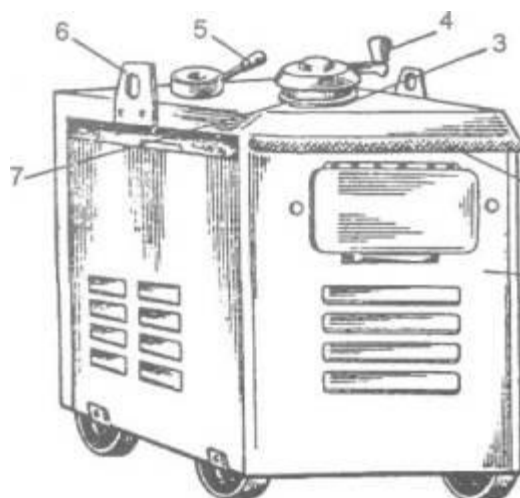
Пересувний зварювальний трансформатор типу ТД:
